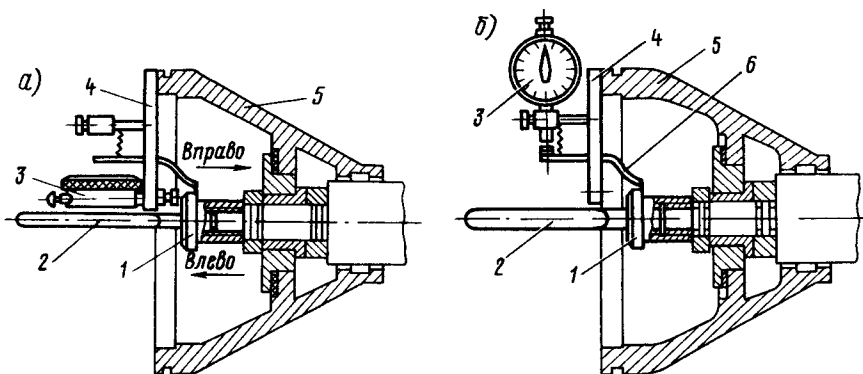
Схема проверки вала ротора турбокомпрессора:
